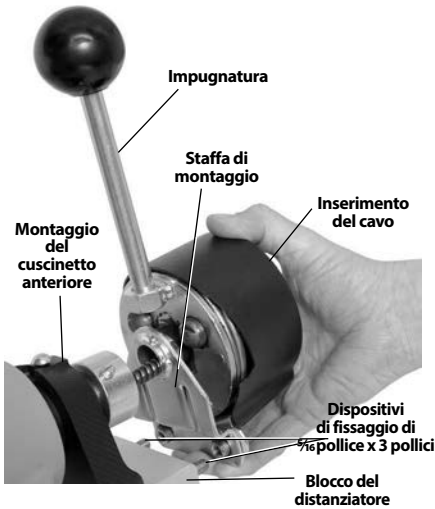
Montaggio dell’Inserimento del cavo sul telaio
